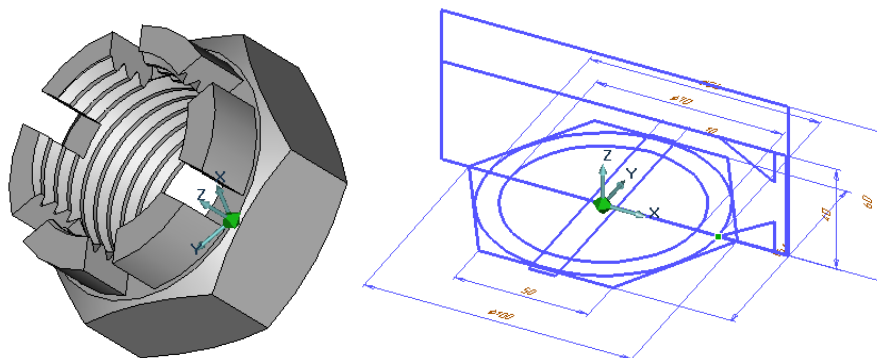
Корончатая гайка и вспомогательные профили для построения ее параметрической модели
